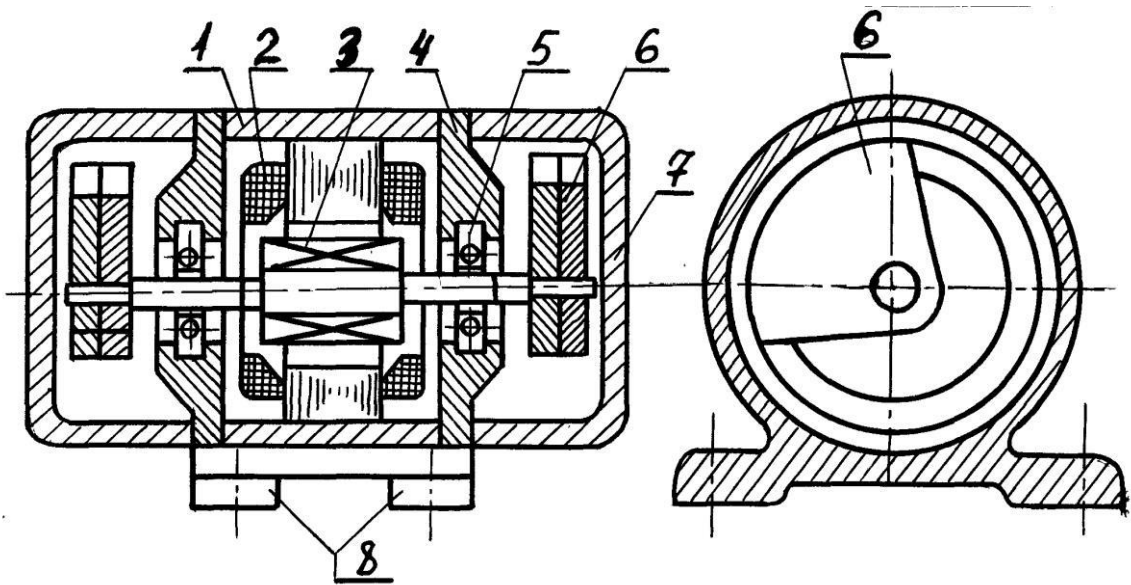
Дебалансний вібратор: 1 - корпус; 2- статор асинхронного двигуна; 3- ротор короткозамкнутий; 4- підшипникові опори; 5- підшипники; 6 - дебаланси; 7-кришка корпусу; 8 - кронштейн для кріплення.
